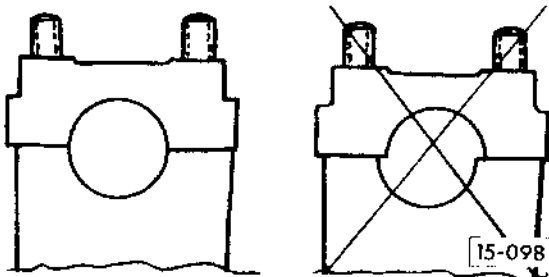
Einbaulage Lagerdeckel-Nockenwelle
